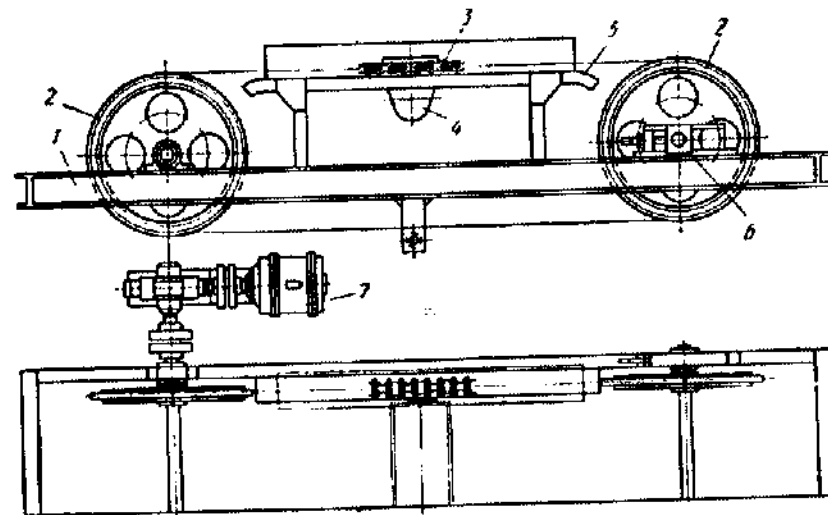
Цепной ковшевый пробоотбиратель с постоянной скоростью движения ковшей: 1 — рама; 2 — цепные колеса; 3 — роликовая цепь; 4 — ковш; 5 — направляющие; 6 — винтовое устройство; 7 — электродвигатель
